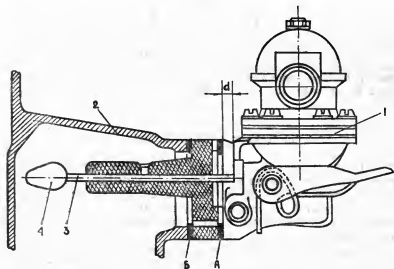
Установка прокладок между корпусом топливного насоса и блоком цилиндров:
